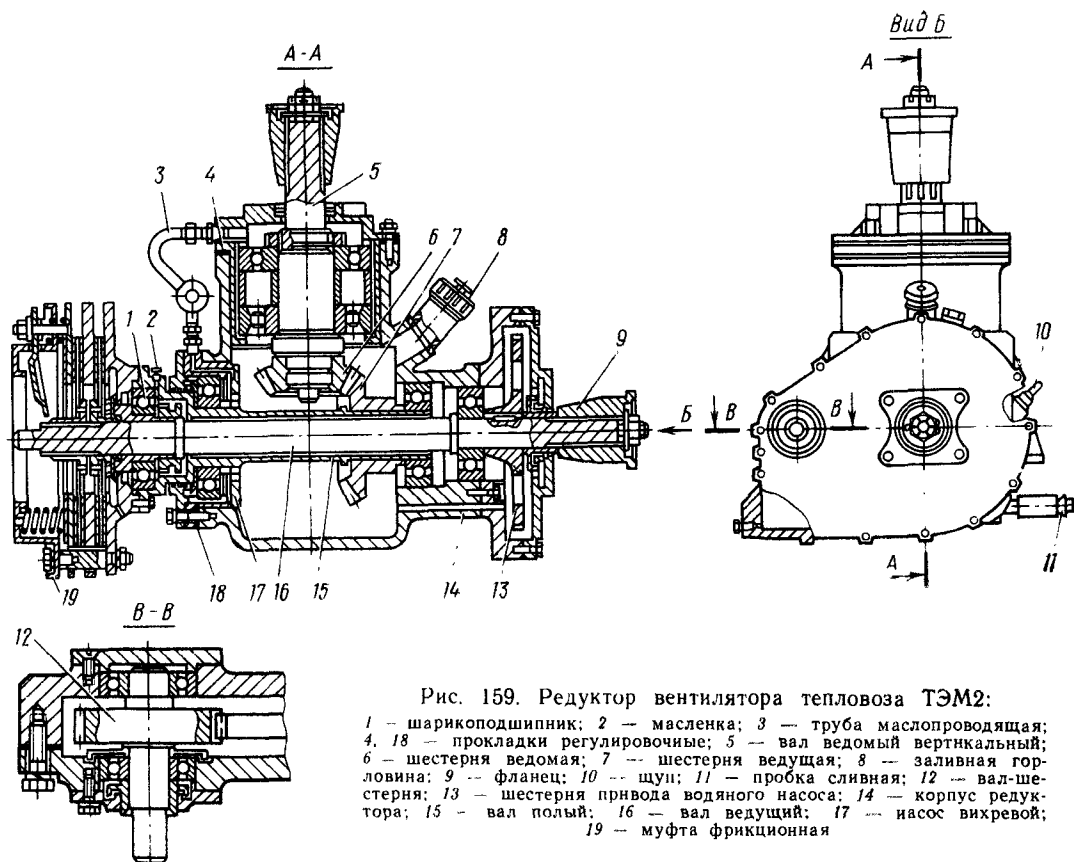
Редуктор вентилятора тепловоза ТЭМ2:
